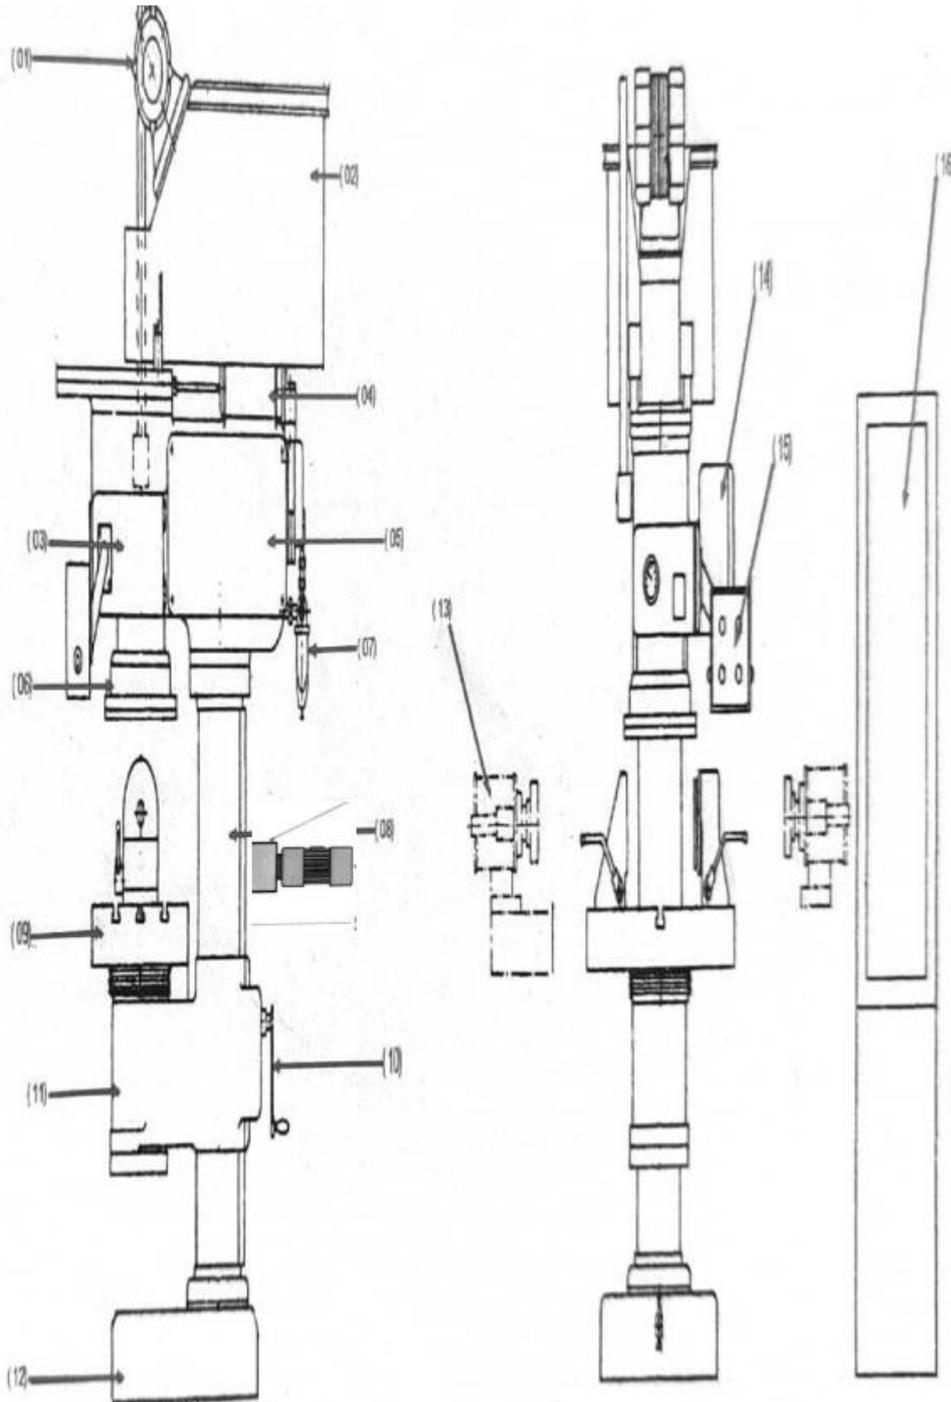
Le schéma d'ensemble de la machine. [1]
